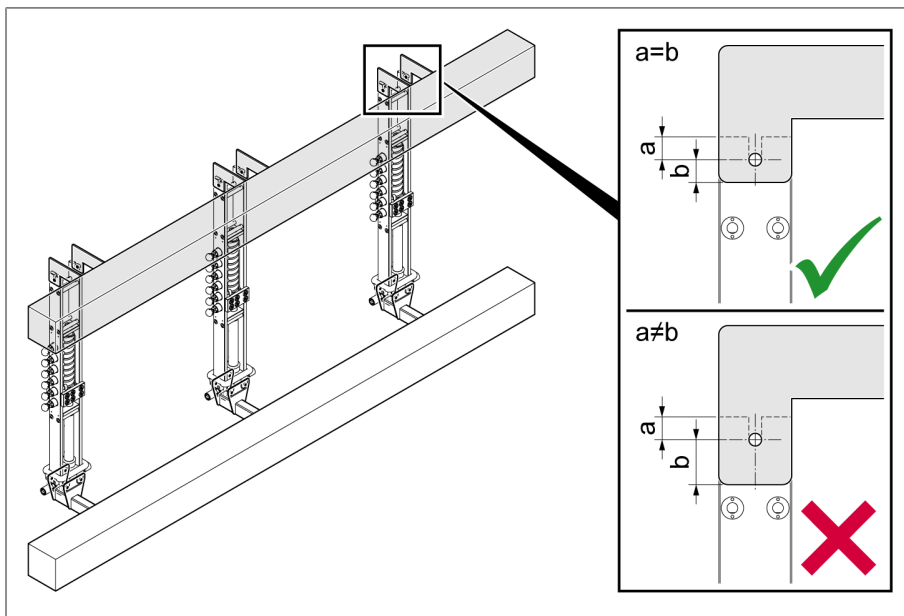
Dispositivo di fissaggio sulla stecca di supporto
